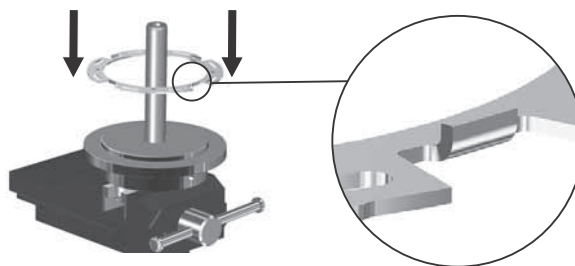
Стопор уплотнительного кольца (65), установленный в приспособление зацепами вверх
